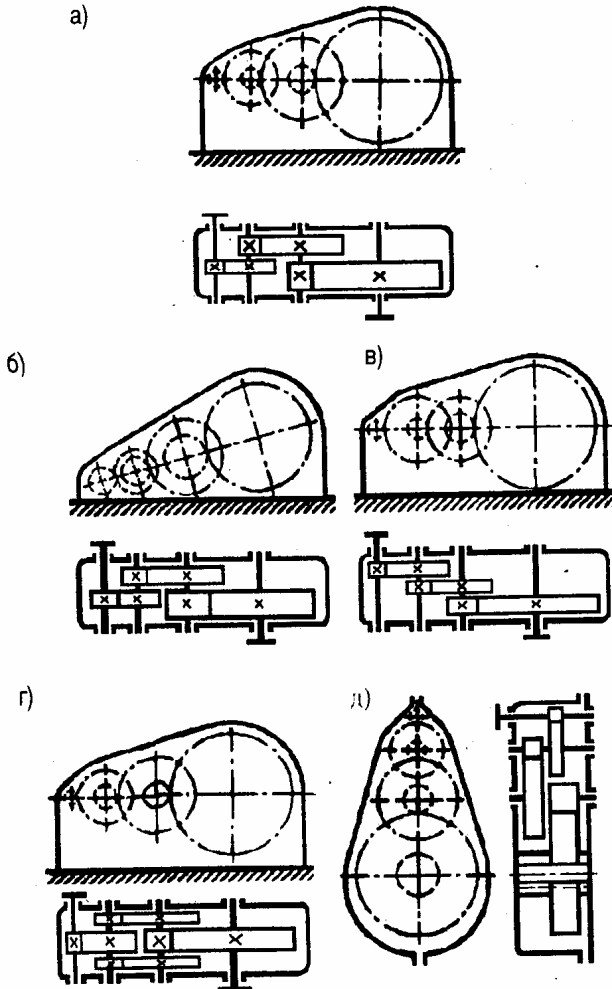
Кинематические схемы цилиндрических трехступенчатых редукторов (ЦЗ)
